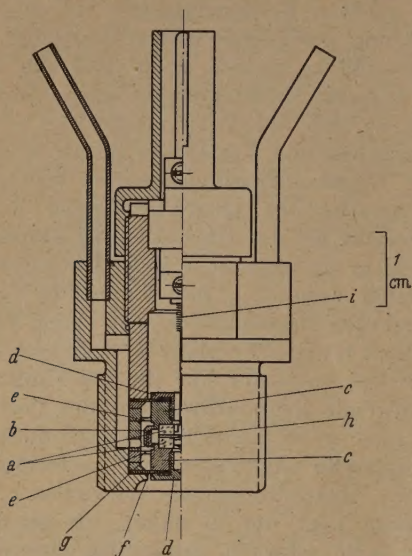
Quarzdruckgeber mit federnd aufgehängtem Meßsystem. *a* Quarzsäule; *b* Federhülse; *c* Widerlager; *d* Halteschrauben; *e* Durchbohrte Aufhängeplattenfedern; *f* Gasabdichtungsmembran; *g* Kühlwasserraum; *h* Abnahmeelektrode, *i* Gewendelter Zuführungsdraht.
